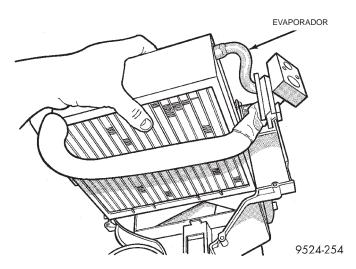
Desmontaje del evaporador de la caja PROBADOR DEL EVAPORADOR
